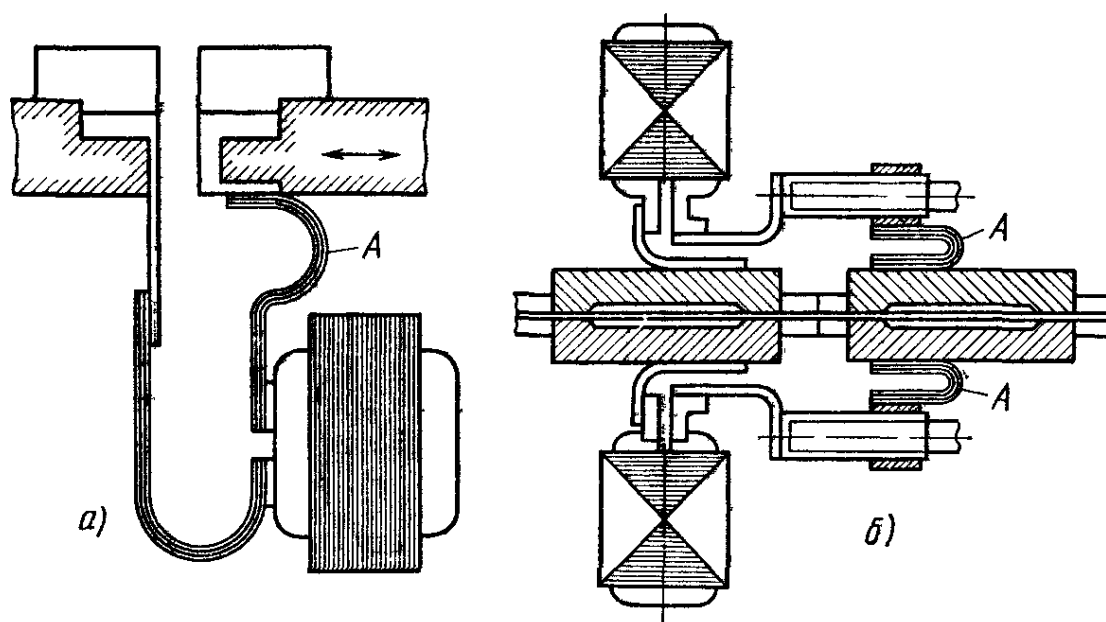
Сварочный контур машины МСМУ-150 (а) и К-255Л (б)
